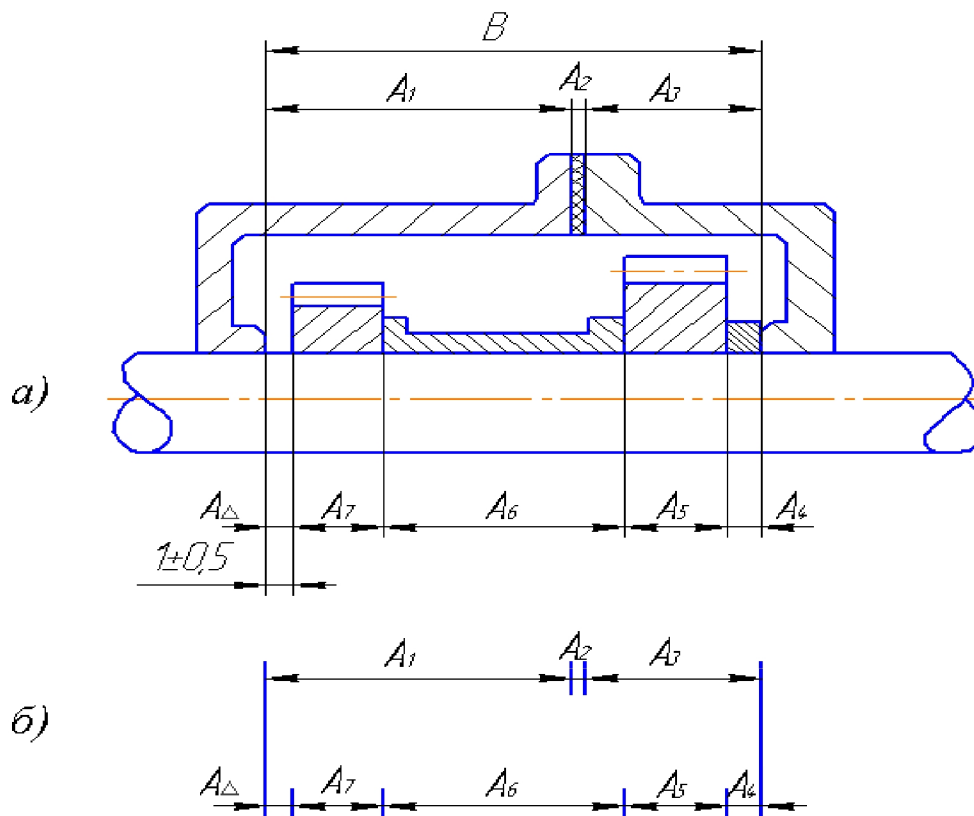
Схема простановки размеров (а) и построения размерной цепи (б) сборочного узла
